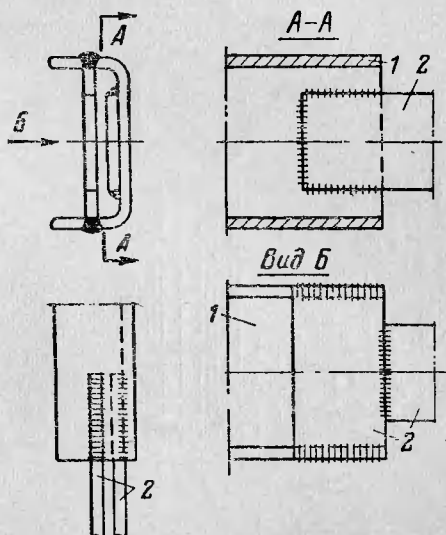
Пример сварного соединения профильной шины с плоской.
